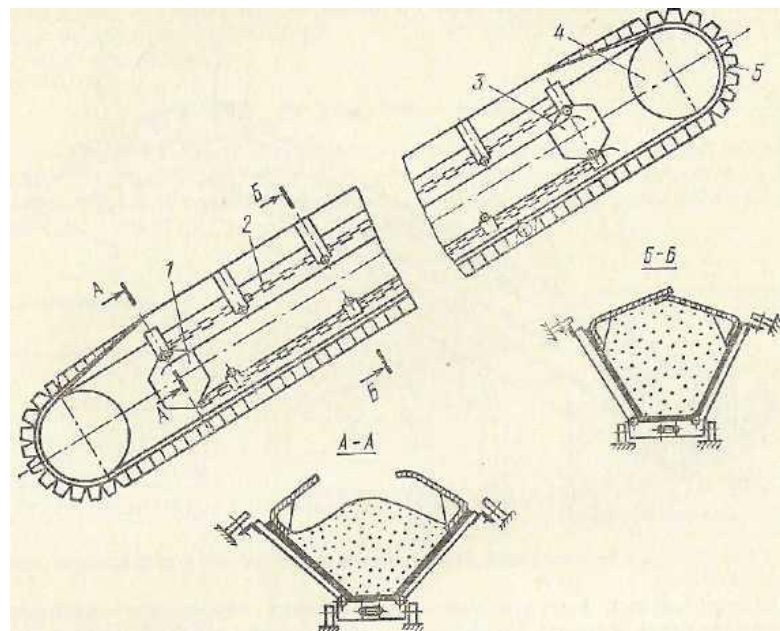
Ленточно-цепной крутонаклонный конвейер с герметизацией перемещаемого груза: 1 — натяжная звездочка; 2 — цепь; 3 — приводная звездочка; 4 - барабан; 5 — лента с бортами
